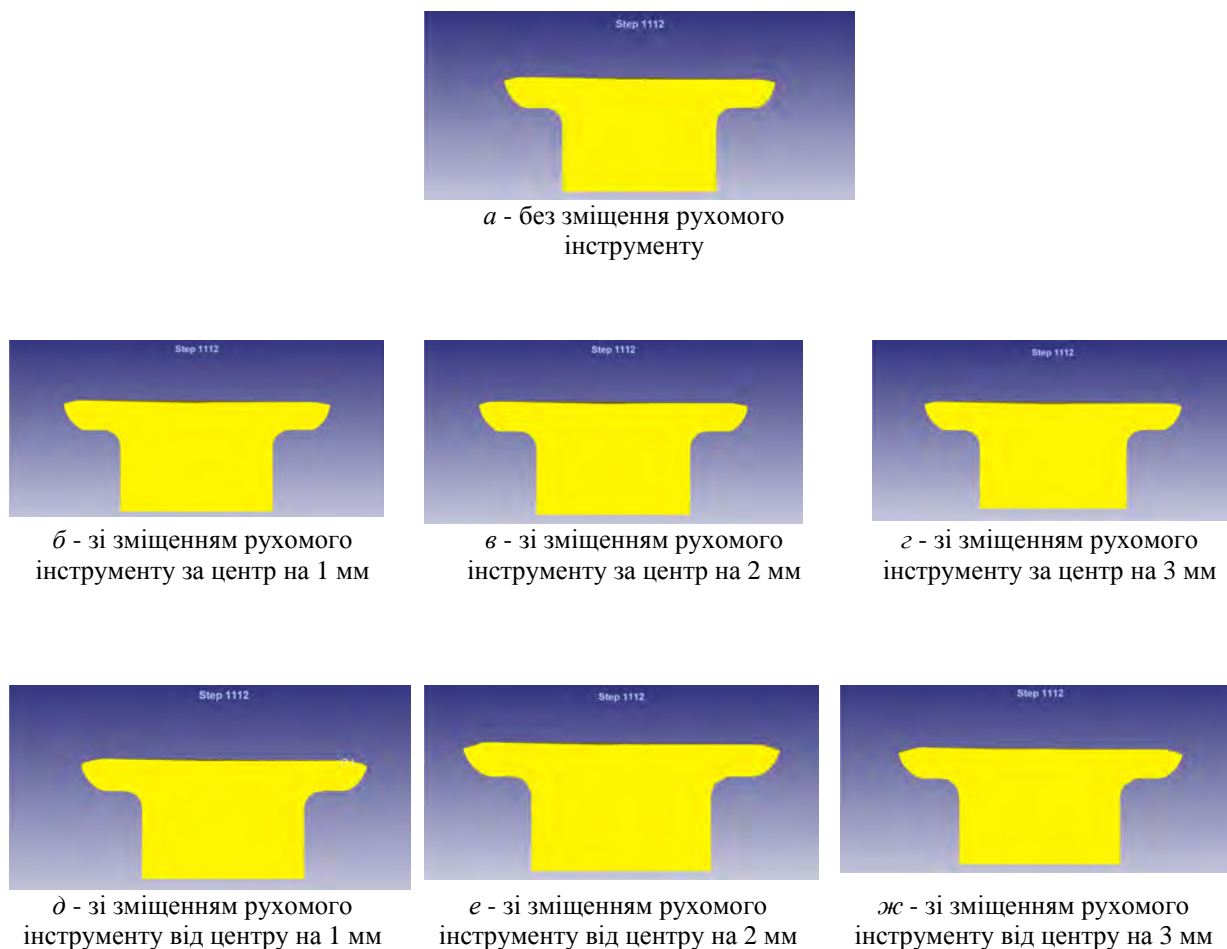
Форма утворюючої бічної поверхні заготовки після пресування без та з цілеспрямованим утворенням активних сил тертя у радіальному напрямку шляхом зміщенням центру обкочування рухомого інструменту за центр або від центру заготовки: *a* – без утворення активних сил тертя; *б, в, г* – із утворення активних сил тертя в напрямку до центра; *д, е, ж* - із утворення активних сил тертя в напрямку від центра
